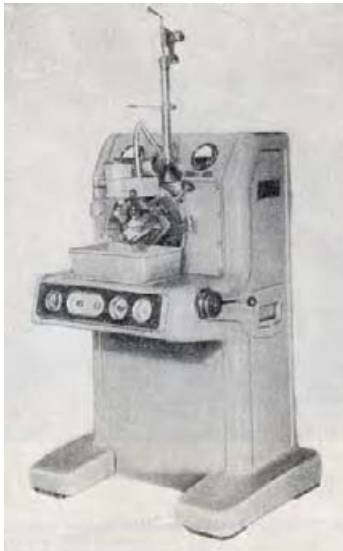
Сверление отверстий  $\varnothing 0,15$  мм в распылителях для насос-форсунок на быстроходном сверлильном станке с пневматическим приводом
